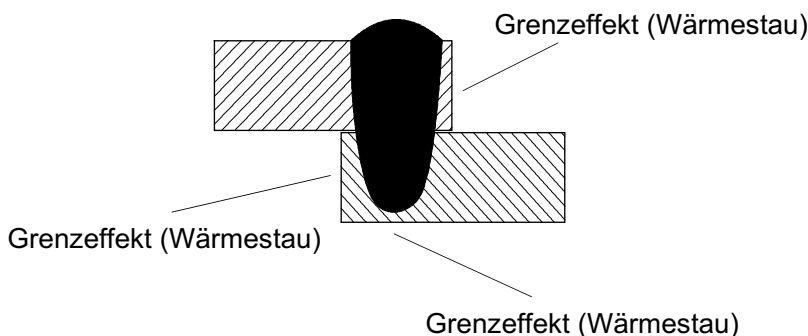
Erläuterung des „Grenzeffektes“ (Wärmestau in den Grenzen des Werkstückes) beim Überlappschweißen.
